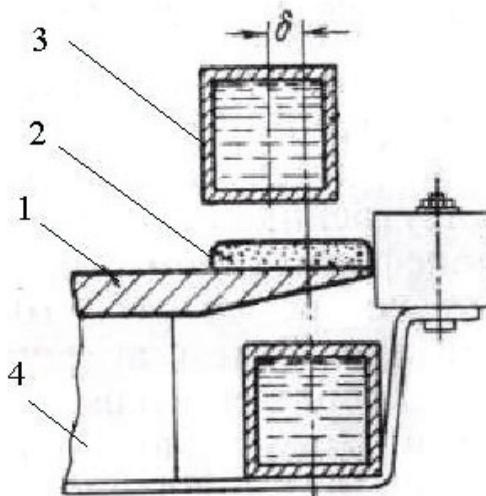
Схема расположения наплавляемой детали в индукторе:
